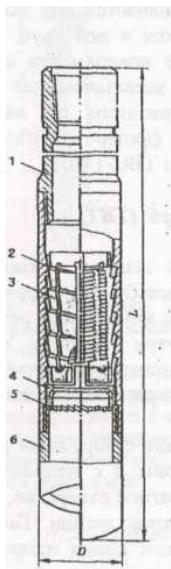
Труболовка наружная освобождающаяся (ТНС): 1-переводник; 2-корпус; 3-втулка захватывающая; 4-уплотнение; 5-фрезер; 6-воронка
